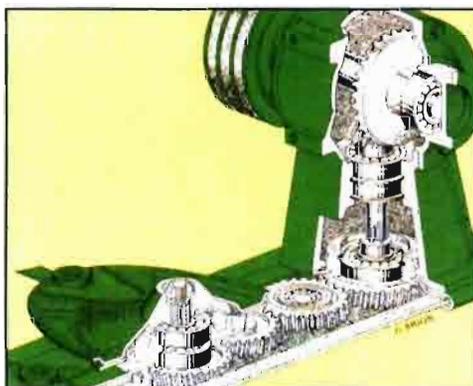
Segadora de discos con transmisión por engranajes. Documentación John Deere.
